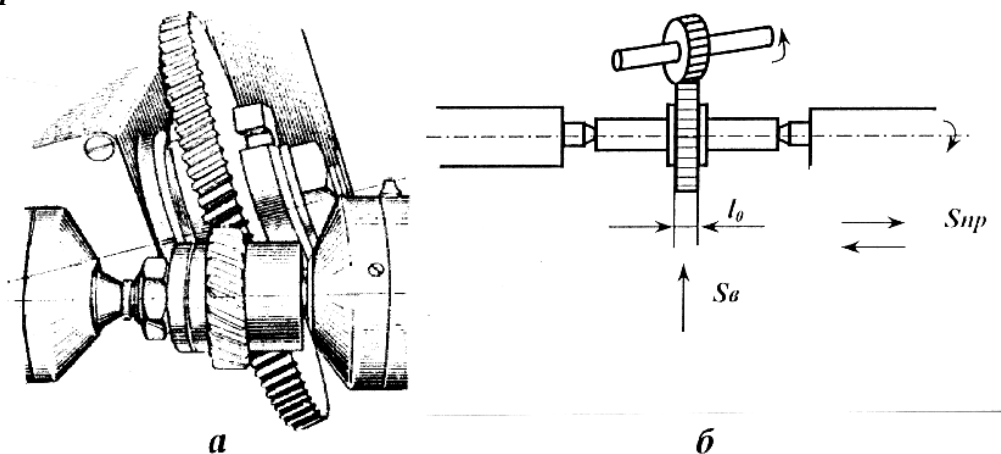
Шевингование цилиндрического зубчатого колеса дисковым шевером: а - общий вид (подача продольная); б - схема шевингования с вертикальным перемещением стола станка.
